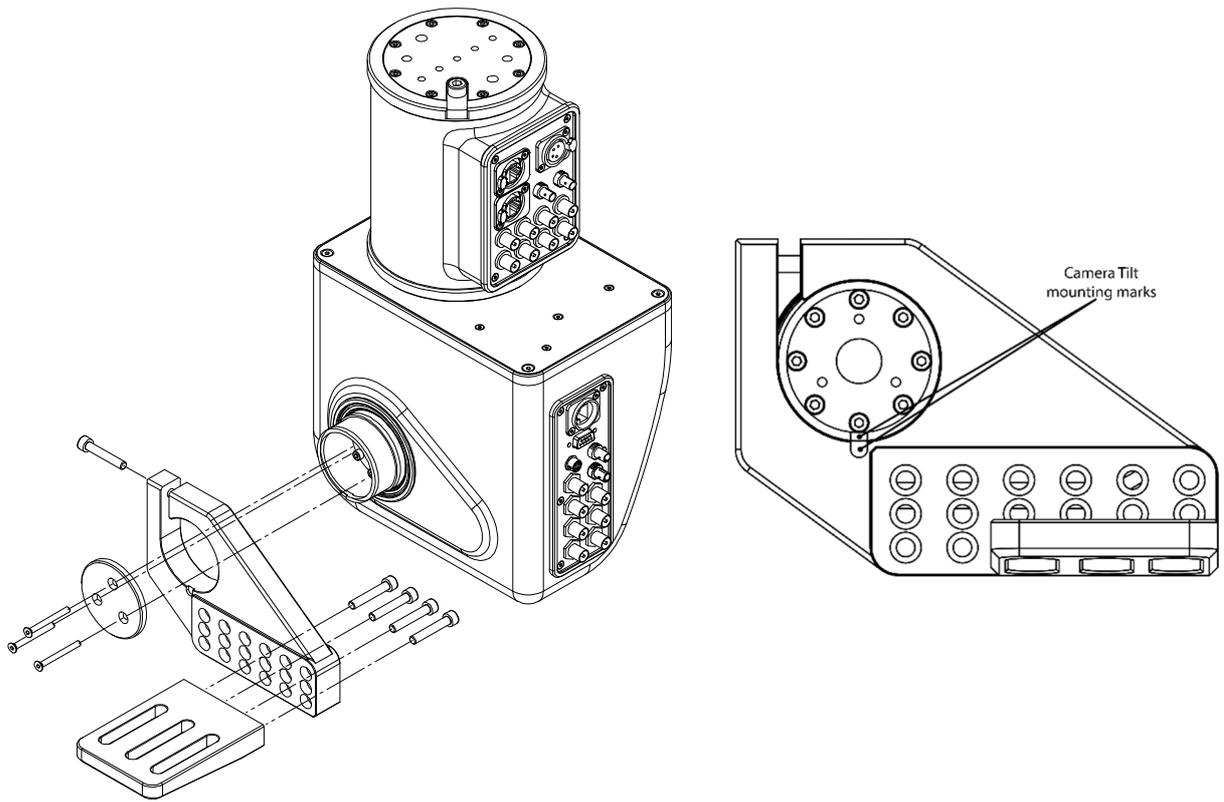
«Обратная» сборка крепления для подвешного монтажа камер, не допускающих переворота изображения
